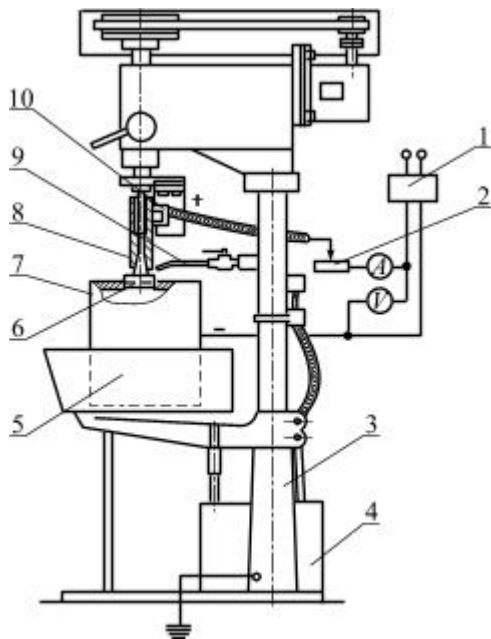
Схема електролігичного натирання обертовою анодною головкою: 1 – випрямляч; 2 – реостат; 3 – свердлильний верстат; 4 – установка для подачі електроліту; 5 – піддон; 6 – анодна головка; 7 – деталь; 8 – патрон; 9 – кран для подачі електроліту; 10 – щіткотримач
